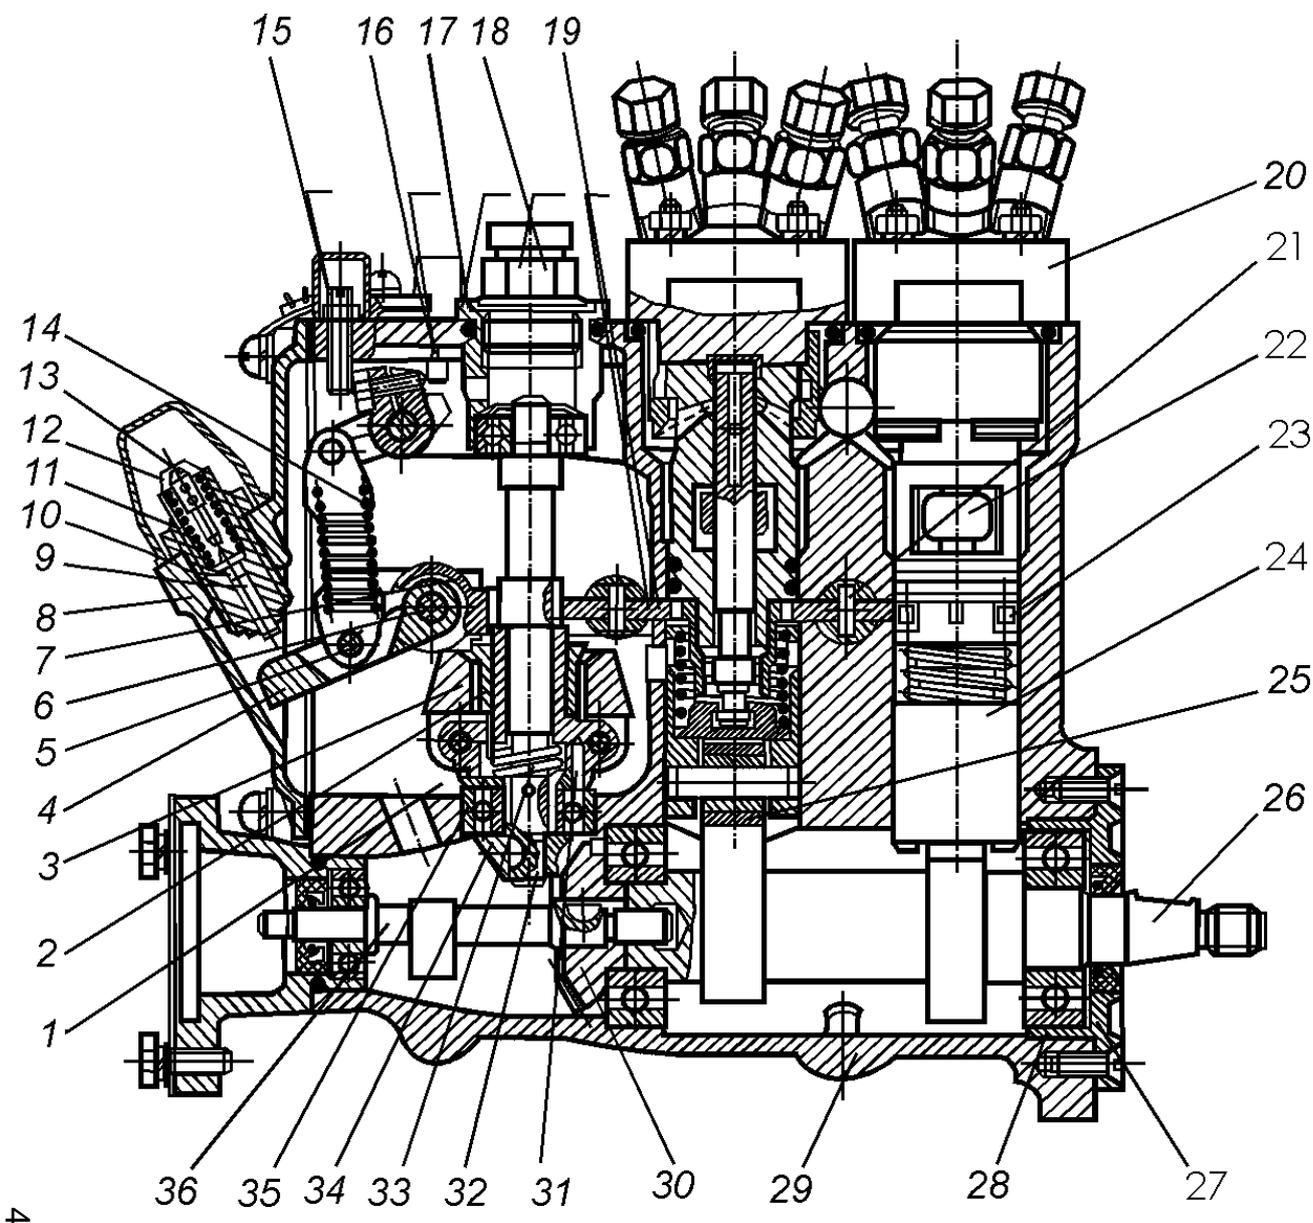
Топливный насос НД-22/6 Б4:
